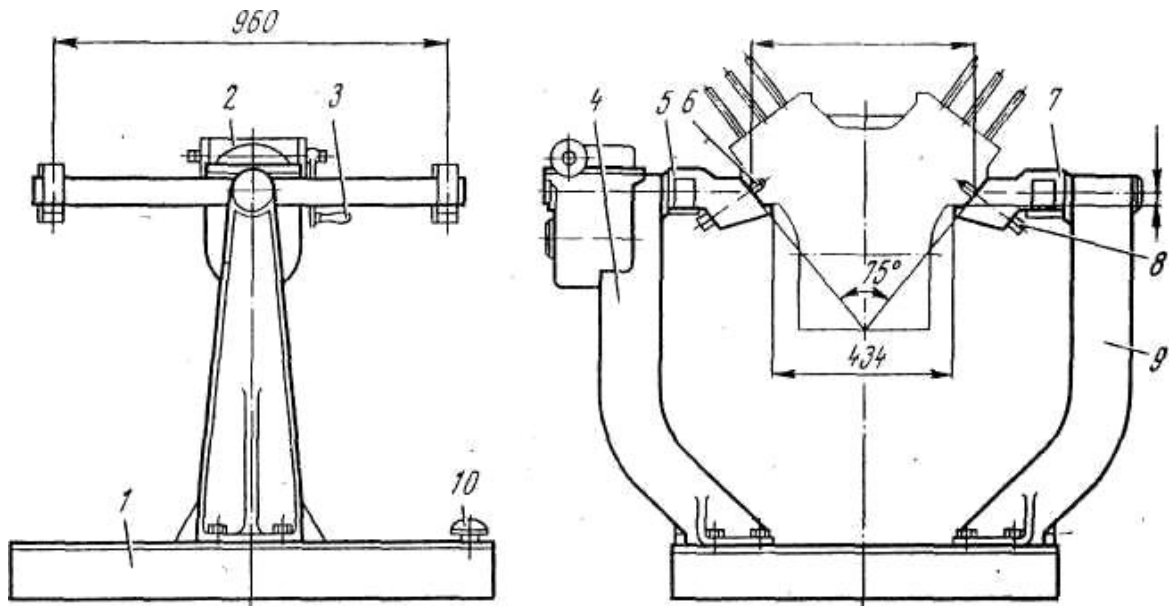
Стенд спеціальний для конструкції ЯМЗ: 1 – станина; 2 – черв'ячний редуктор; 3 – рукоятка редуктора; 4, 9 – стійки; 5, 7 – поворотні балки; 6, 8 – установчі пальці; 10 – педаль фіксатора.
